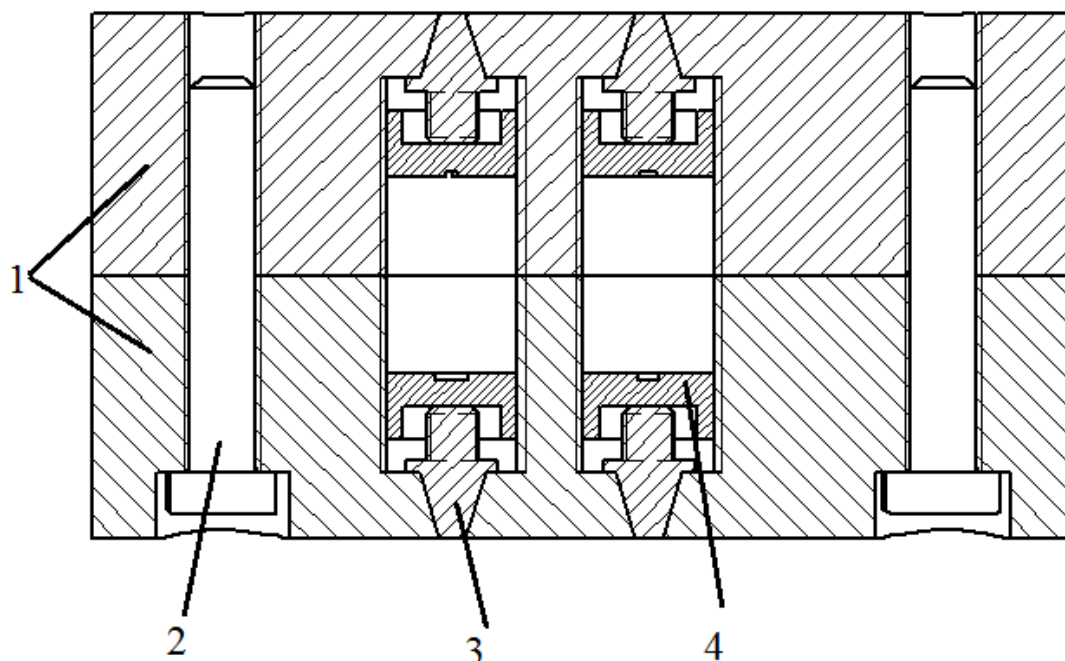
Разборный цилиндрический образец: 1 – полублок, 2 – винт, 3 – конический штифт, 4 – поджимная пробка
